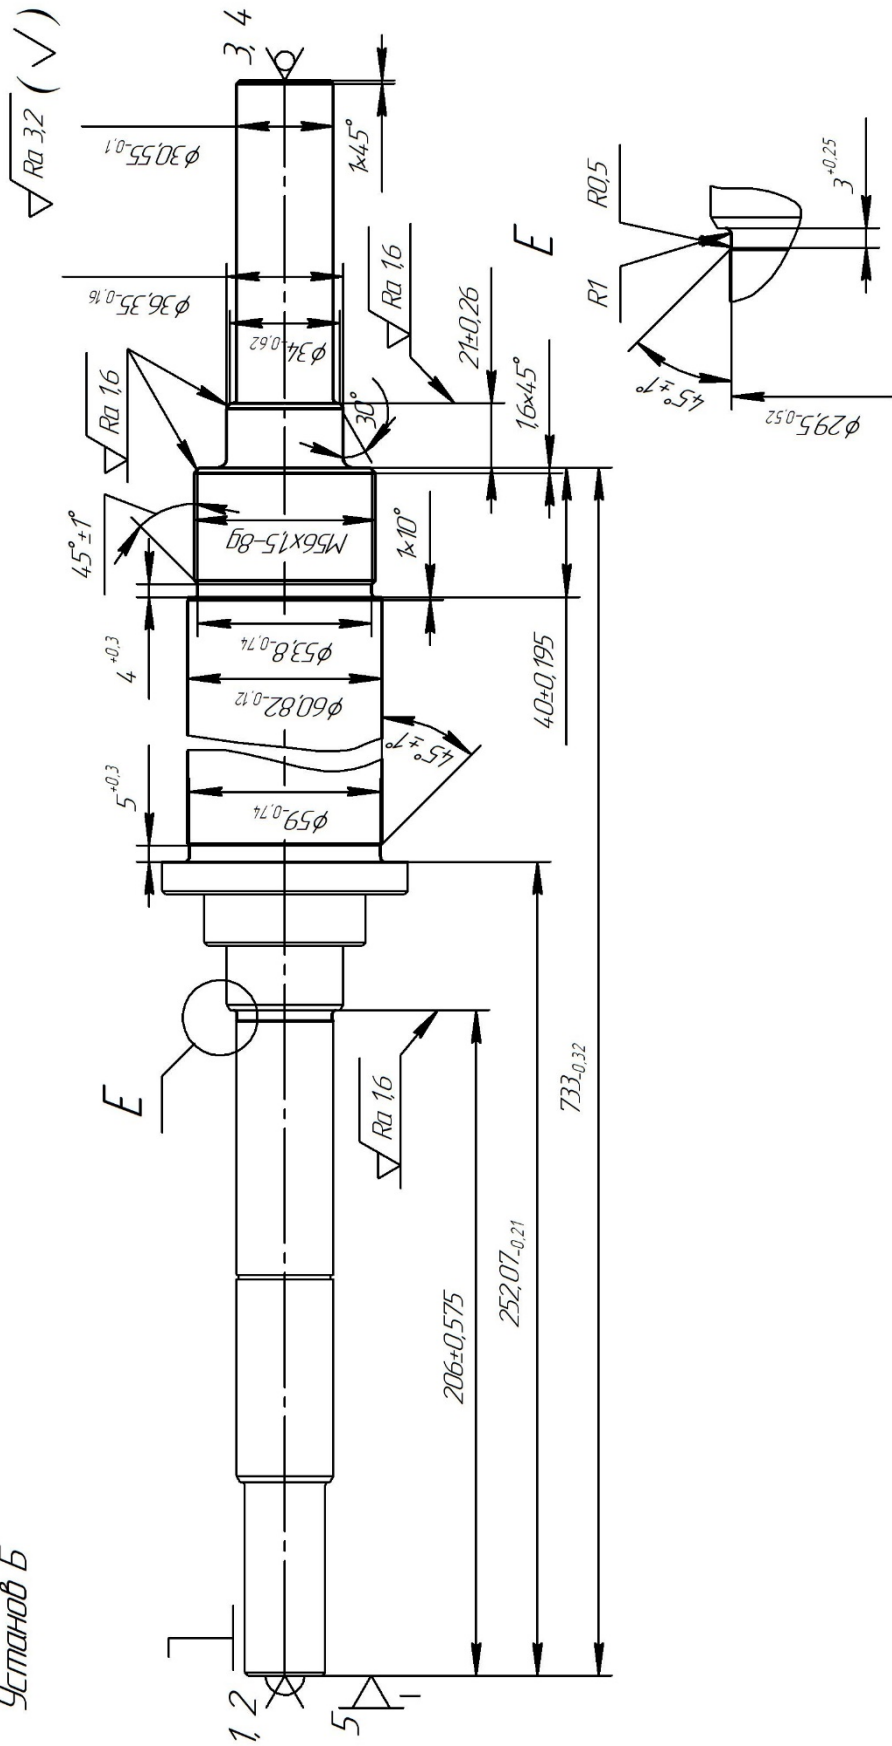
Схема базування заготовки на операції токарній з ЧП,К 025, установ Б
